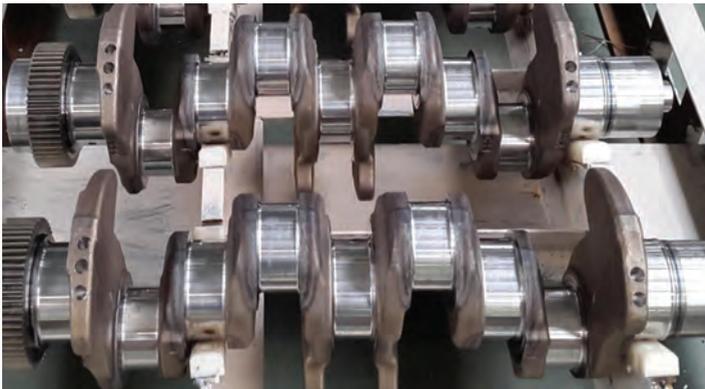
Обработанные коленчатые валы 4 - х цилиндрического двигателя. Отверстия в противовесах, выполненные при балансировке вала, расположены с одной половины вала, прилегающей к обрезному пуансону при обрезке облоя.
